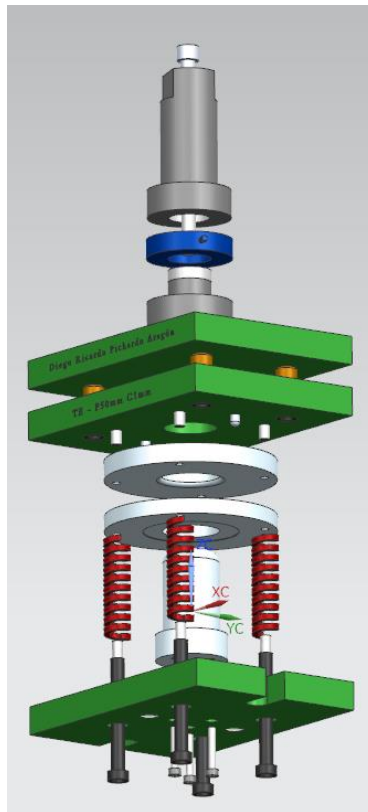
Dibujo del troquel de embutido ensamblado.
